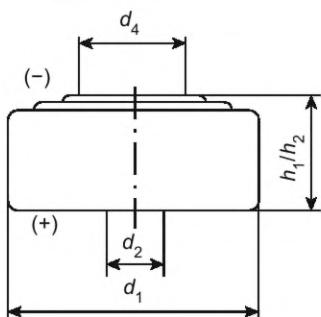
Габаритный чертеж PR70, PR41, PR48, PR44, PR1154
